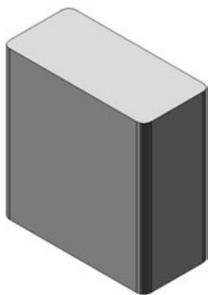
Геометрическая модель формы заготовки изделия “Кронштейн”
